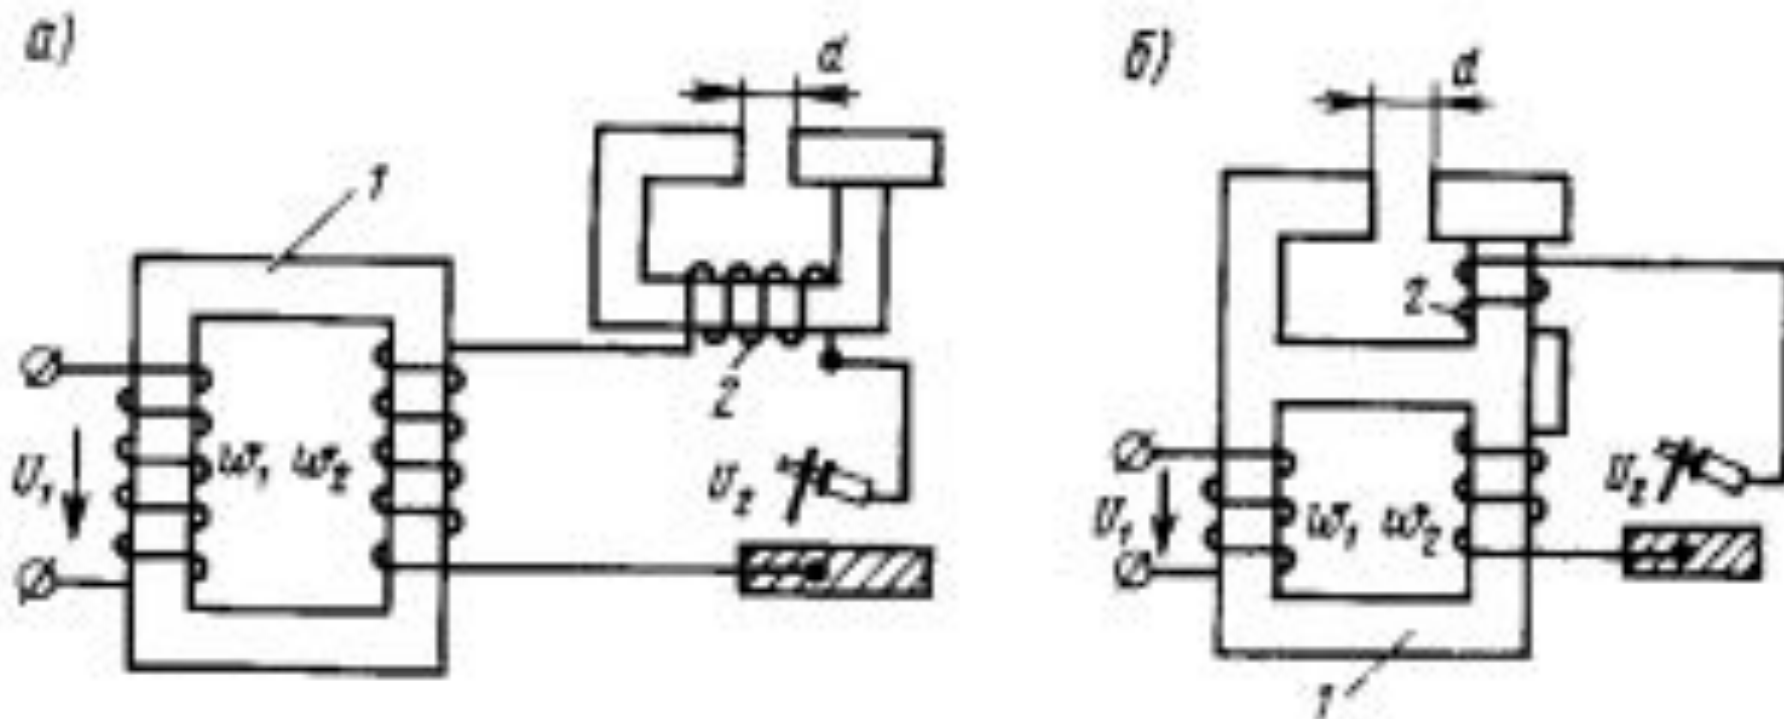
Принципиальные схемы сварочных трансформаторов: а — с внешней индуктивностью (реактором), б — с реактором на общем сердечнике;
